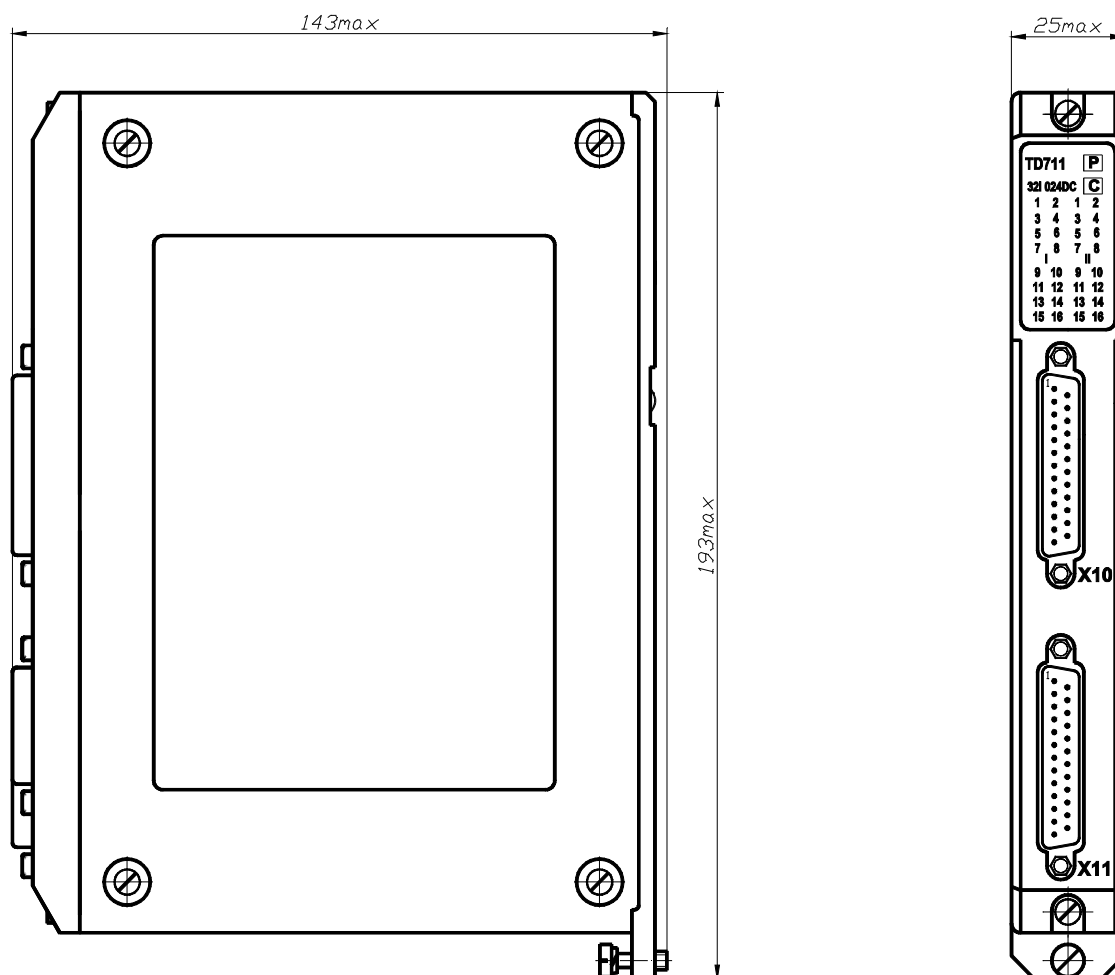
Внешний вид и габаритные размеры модуля TD 711
